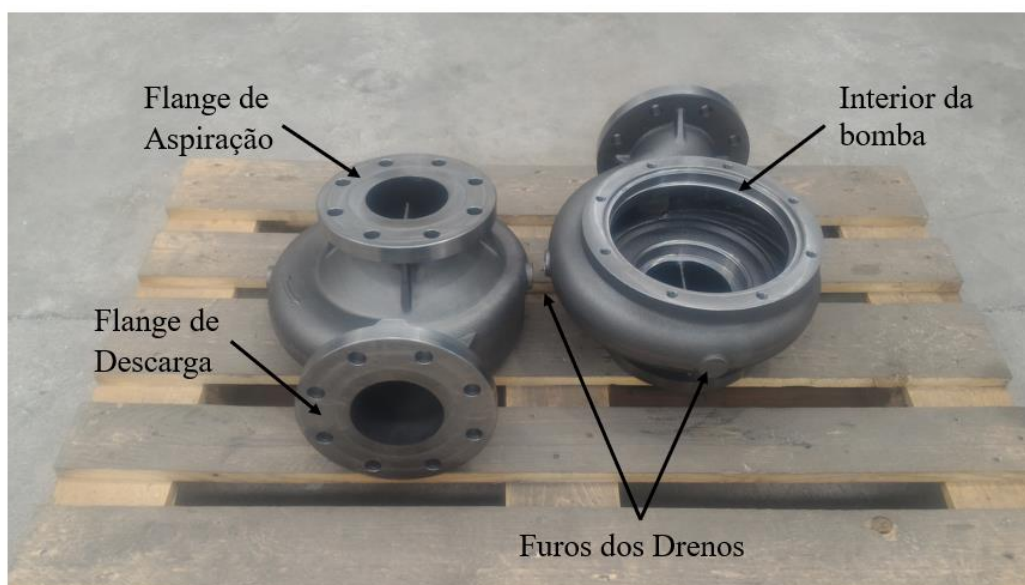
Partes a maquinar do corpo da bomba TGCL100L.
